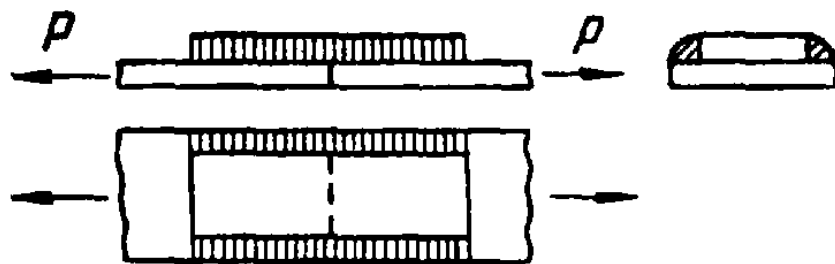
Сварное соединение с фланговыми швами.
